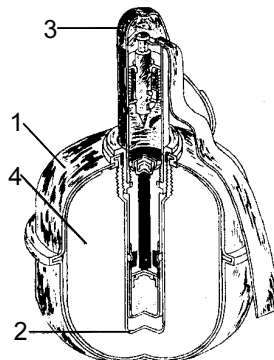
Граната РГД-5: 1 - корпус; 2 - трубка для запалу; 3 - запал; 4 - розривний заряд
